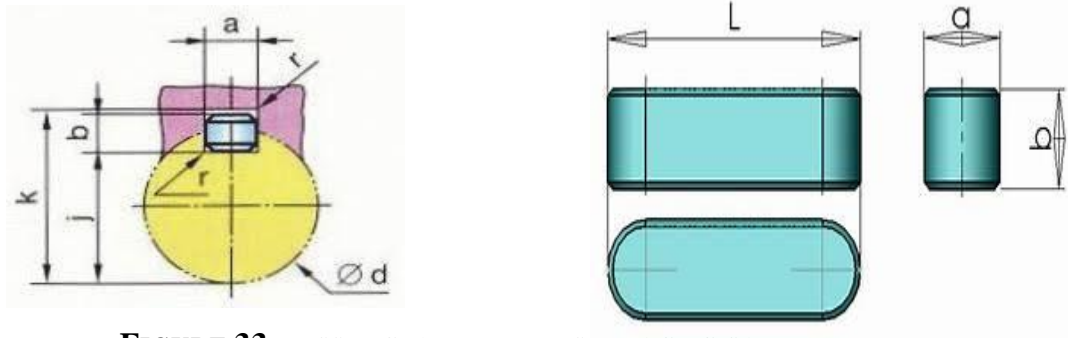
DESSIN CLAVETTE ET SURFACE CISAILLER
